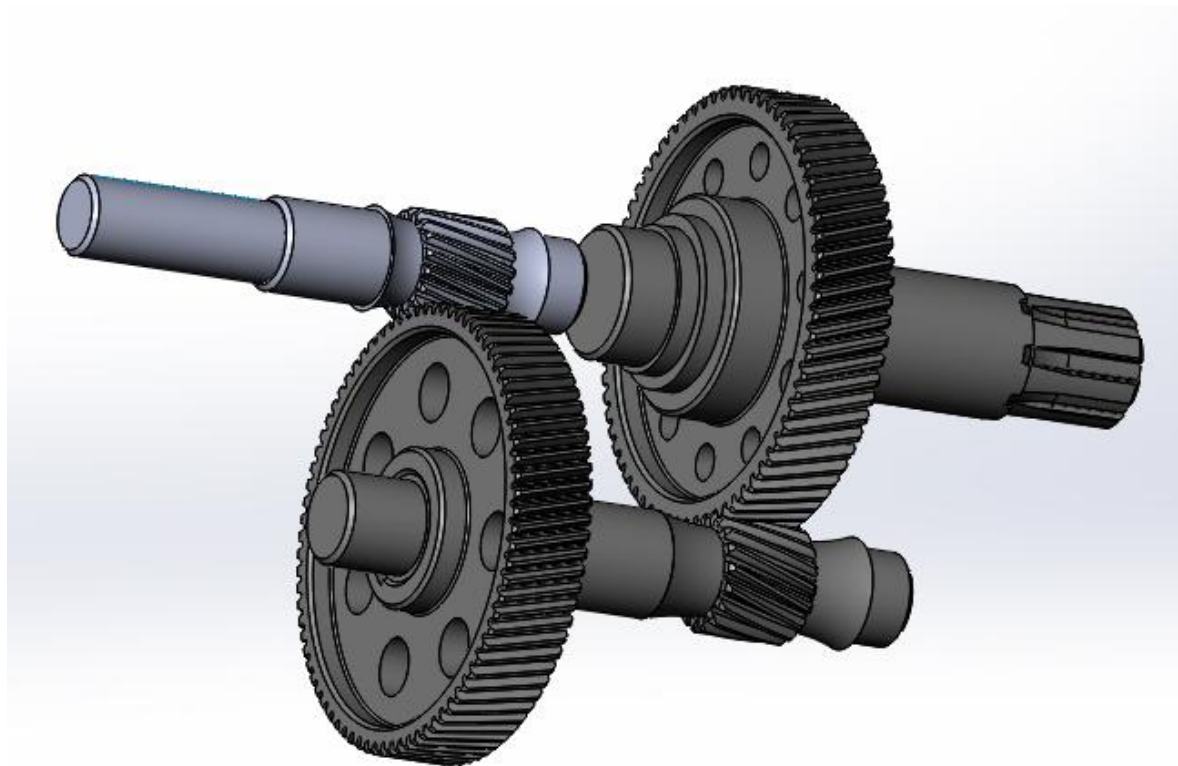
3Dмодель цилиндрической соосной двухступенчатой зубчатой передачи в SOLIDWORKS.
